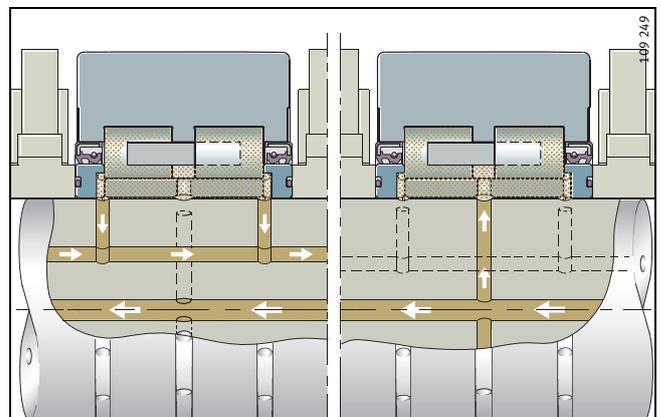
· Ölumlaufschmierung – Stützrolle mit Wellendichtung
